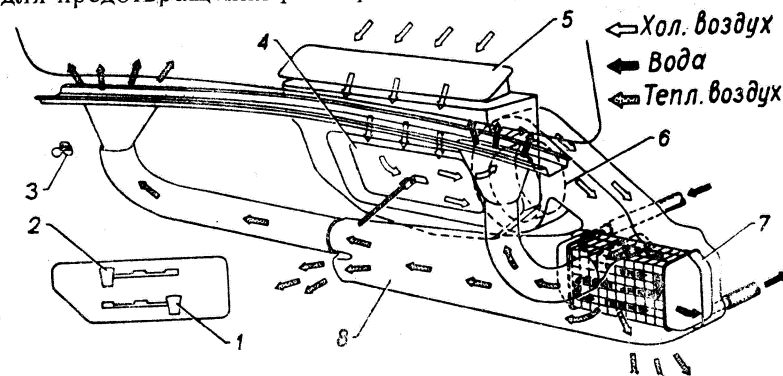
Отопление и вентиляция кабины и обдув ветрового стекла. 1—рукоятка крышки воздухопритока, 2—рукоятка крышки внутреннего люка, 3—переключатель, 4—крышка внутреннего люка, 5—крышка люка воздухопритока, 6—вентилятор с электродвигателем, 7—радиатор отопителя, 8—распределитель.
